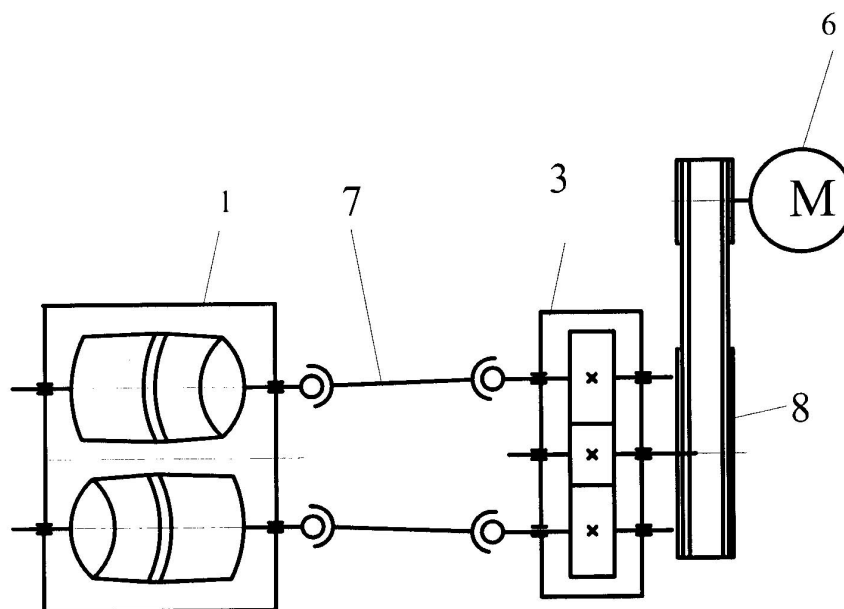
Главная линия клетки поперечно-винтовой прокатки с групповым приводом бочкообразных валков
